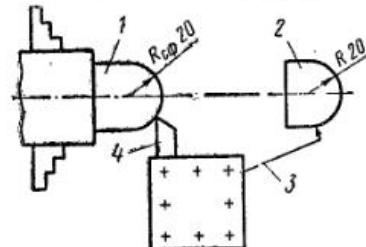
Приспособление на станине для обработки сферических поверхностей:
